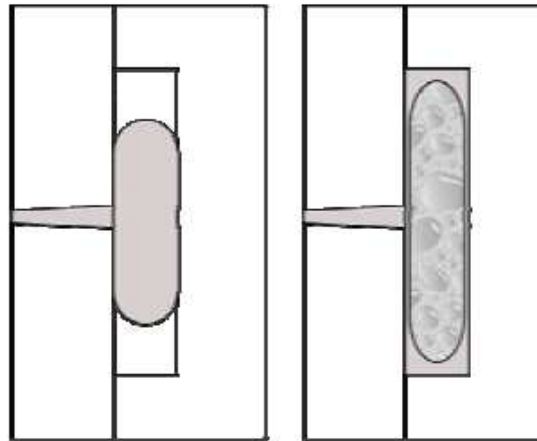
Moldagem de injeção com expansores químicos a baixa-pressão [20].
